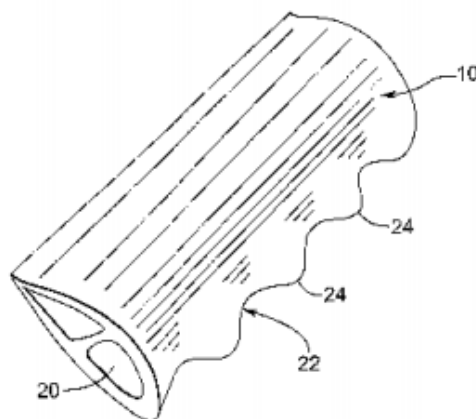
Dibujo de la patente EP1805412. Fuente: EP1805412, Stephen Dewar, Turbine and compressor employing tubercle leading edge rotor design, 2016
